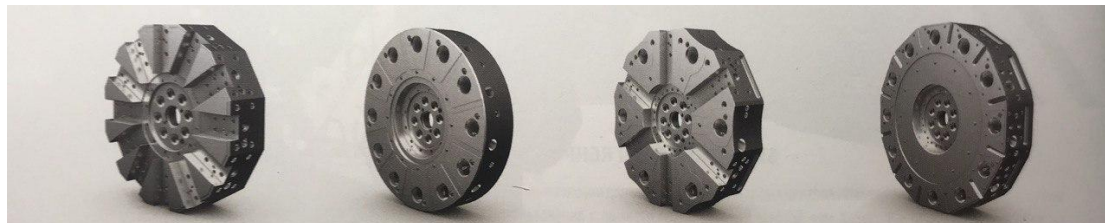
Багатопозиційний інструментальний магазин
